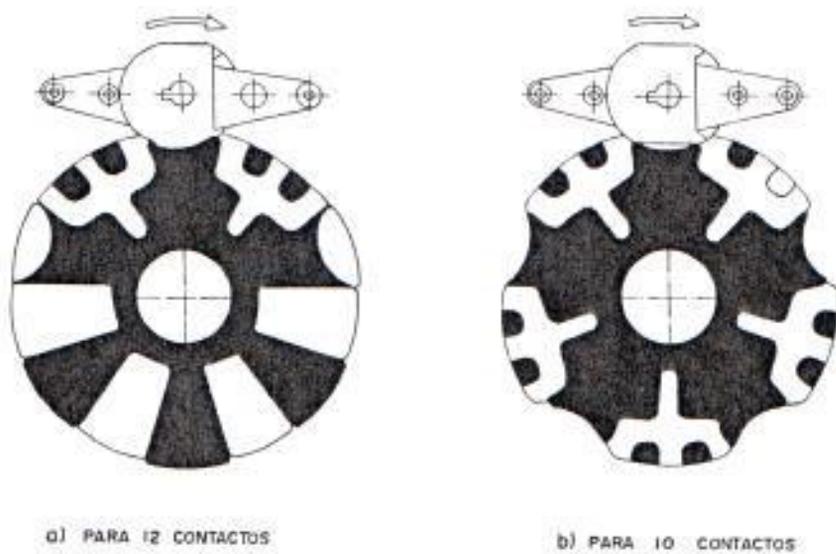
ENGRANAJE GENEVA PARA EL MOVIMIENTO DEL SELECTOR
